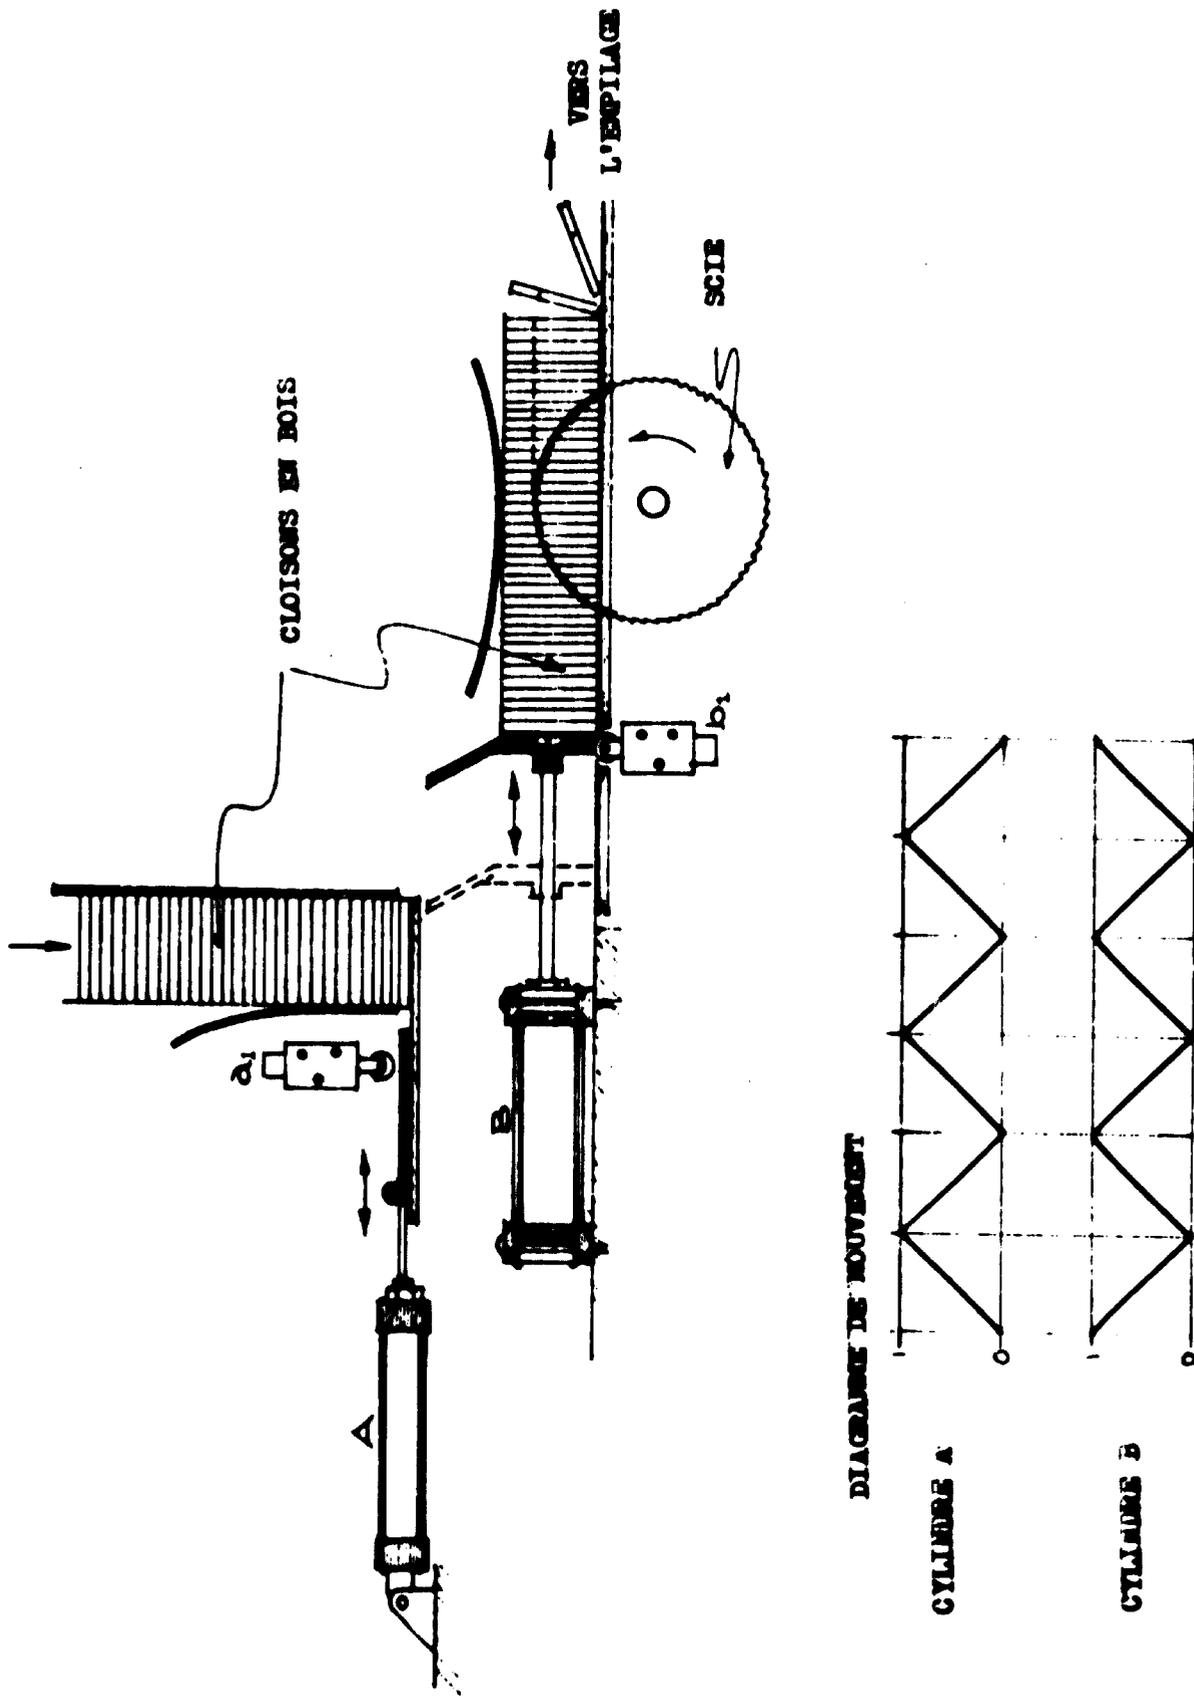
Machine à entailler les cloisons de casiers à bouteilles:vue latérale et diagramme temps/mouvement
